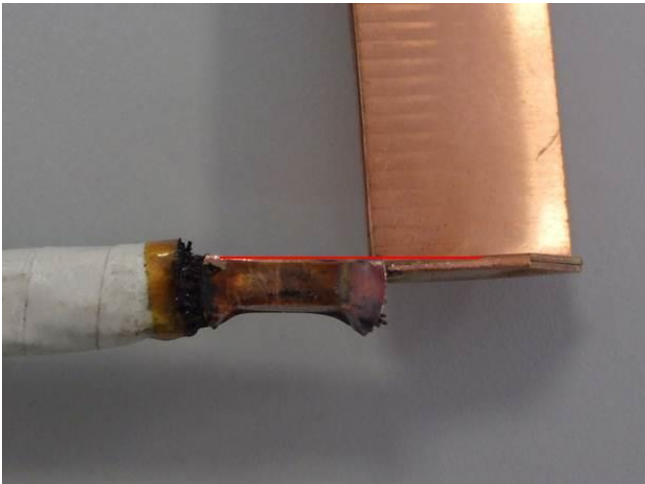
Kontaktierung mittels Widerstandsschweißen
